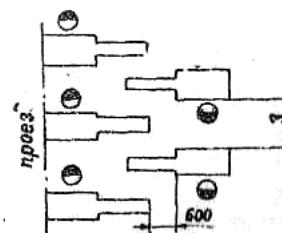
Расстояние 3 между токарными автоматами и револьверными станками, расположенными в затылок
